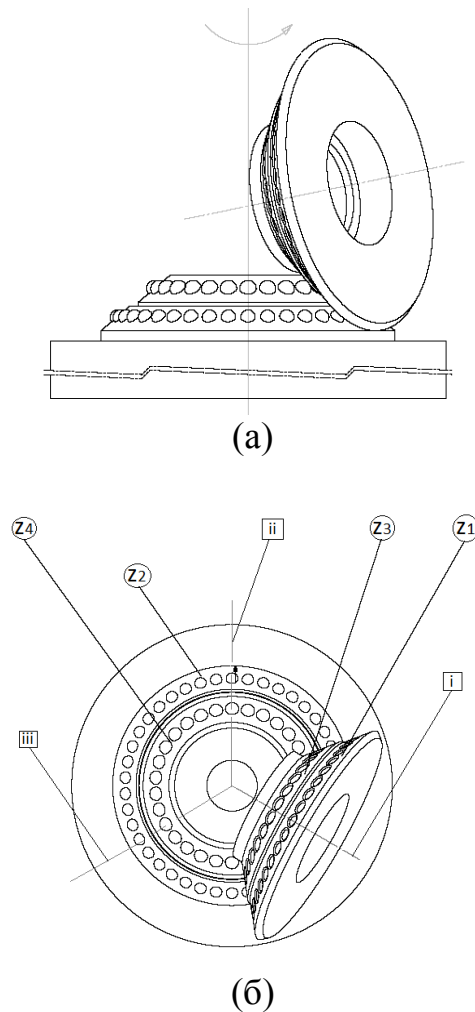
Зацепление колеса и шестерни: а – вид спереди; б – вид сверху (колеса ii и iii показаны условно)
